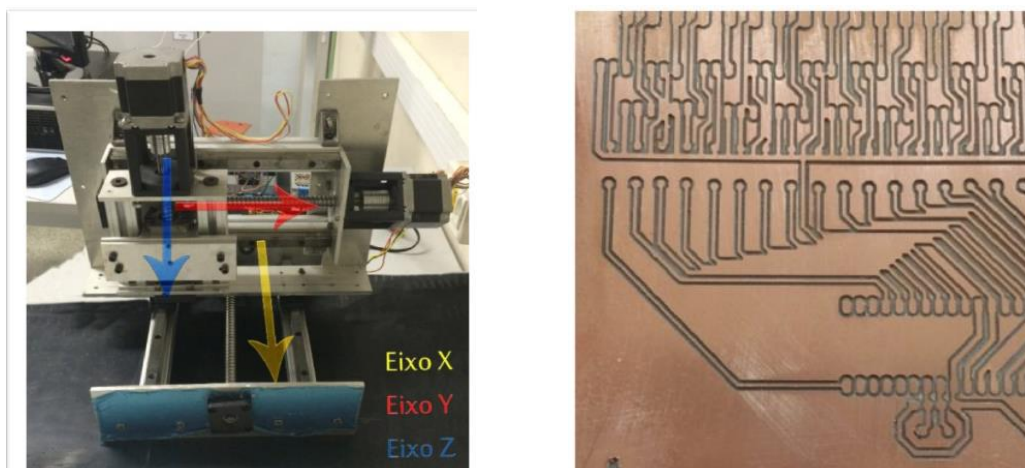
Máquina para fabricação de placa de circuito impresso (esquerda) e placa de circuito impresso feita na máquina de PCI (direita) (Yuri, Jander e Lucas, 2015)
